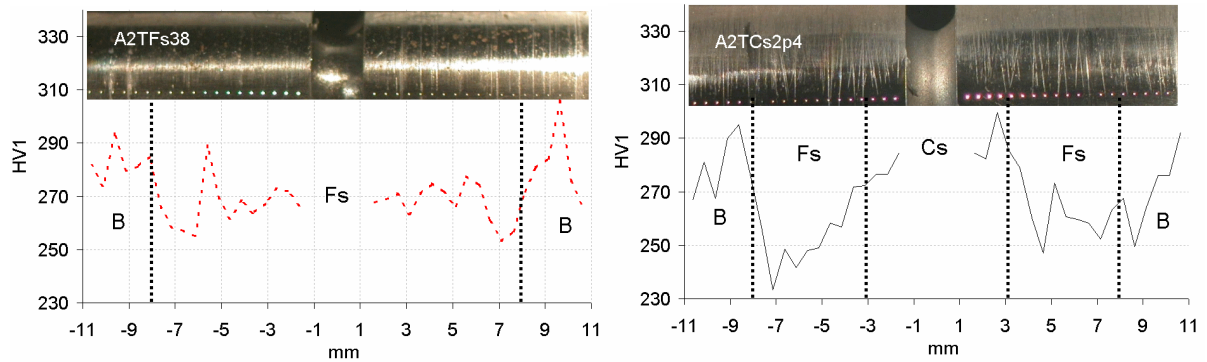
Vérification de la taille des zones chauffées sur machine Gleeble : Fs sur 16 mm et Cs sur 6 mm (les mesures ont été réalisées sur le fût des éprouvettes usinées)
